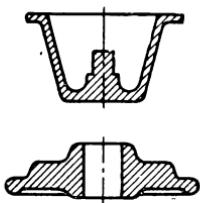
Примерные конструкции деталей из алюминиевых и магниевых сплавов
